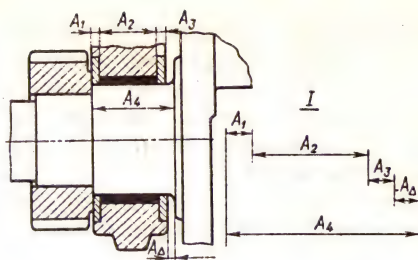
Сопряжение передней коренной шейки коленчатого вала двигателя ЗИЛ-130:
